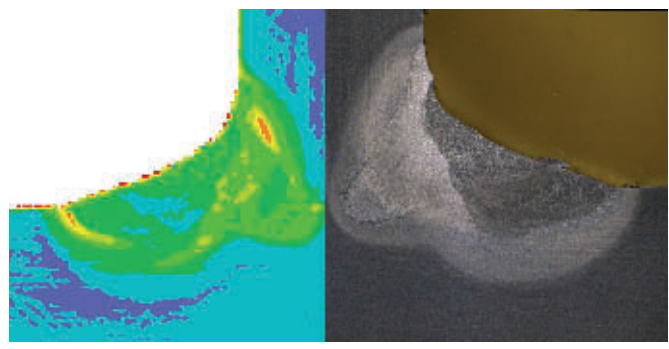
Makroschliff und Härtemessung einer reparaturgeschweißten Schwingprobe [1]
